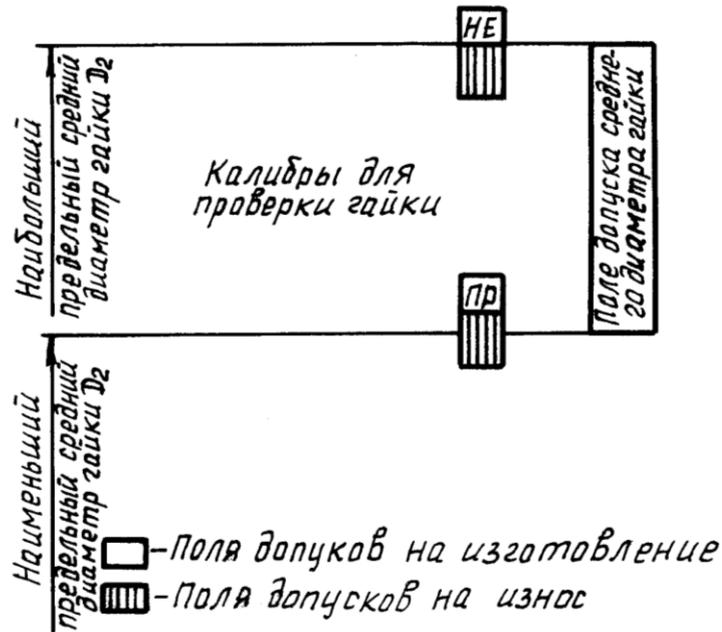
Схема расположения полей допусков среднего диаметра калибров для проверки гаек
